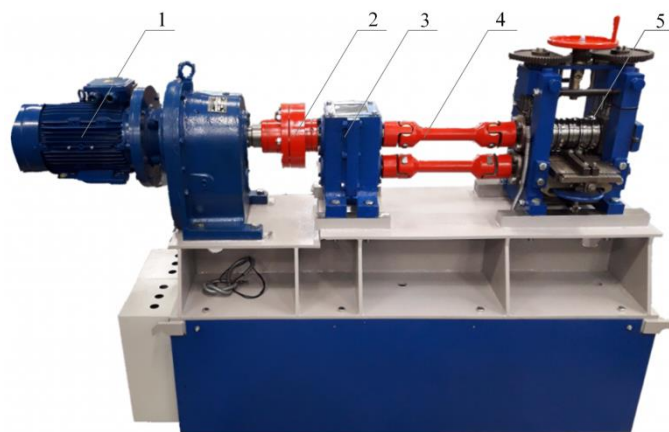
Лабораторный прокатный стан ДУО-130: 1 – мотор-редуктор; 2 – втулочно-пальцевая муфта; 3 – шестеренная клеть; 4 – универсальные шпиндели; 5 – рабочая клеть
